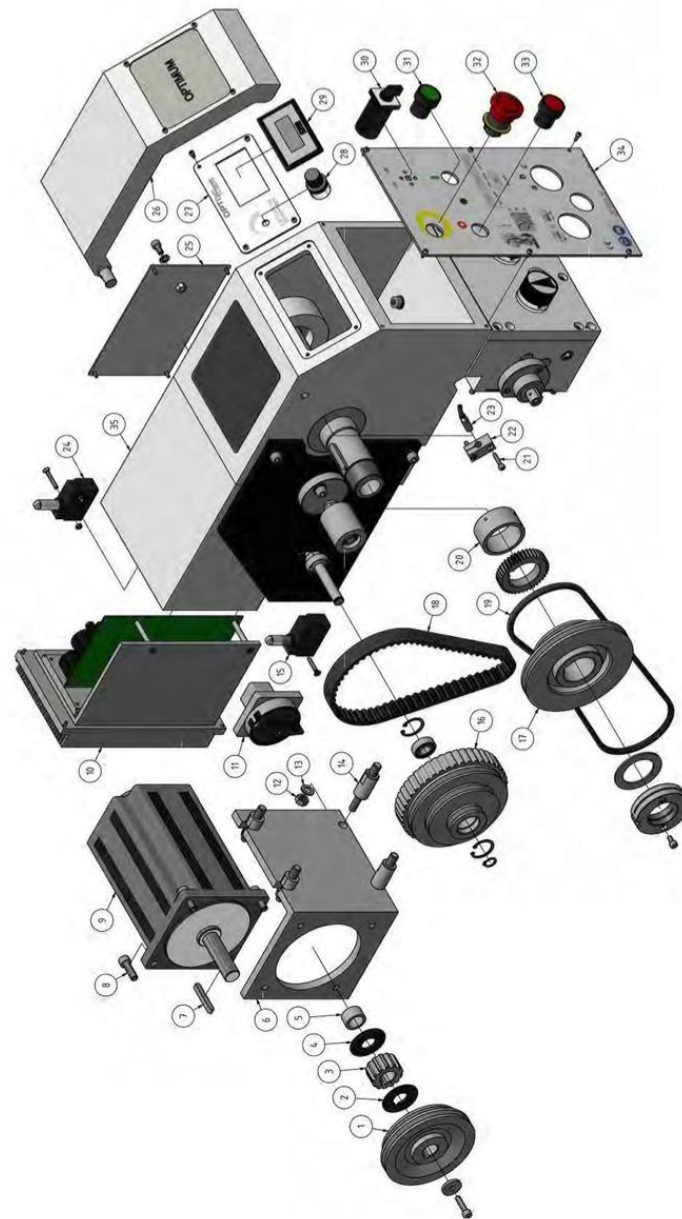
Spindelstock - Cabezal TU 2807 V
